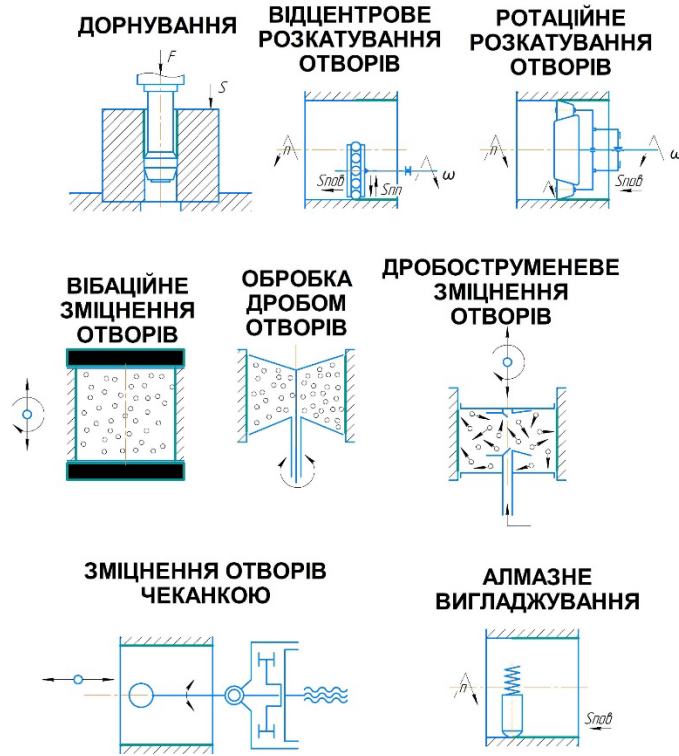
Обробка отворів методами поверхнево-пластичного деформування
